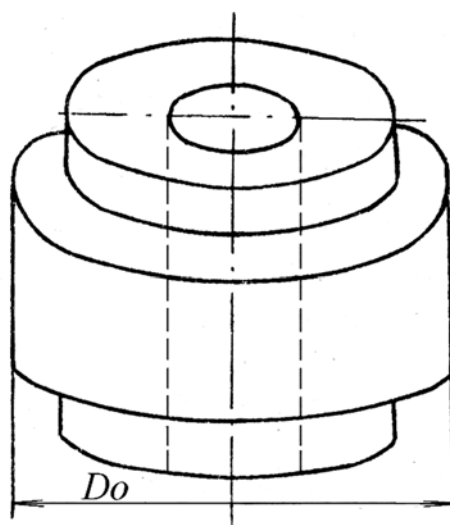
Общий вид отливки с вертикальным отверстием
